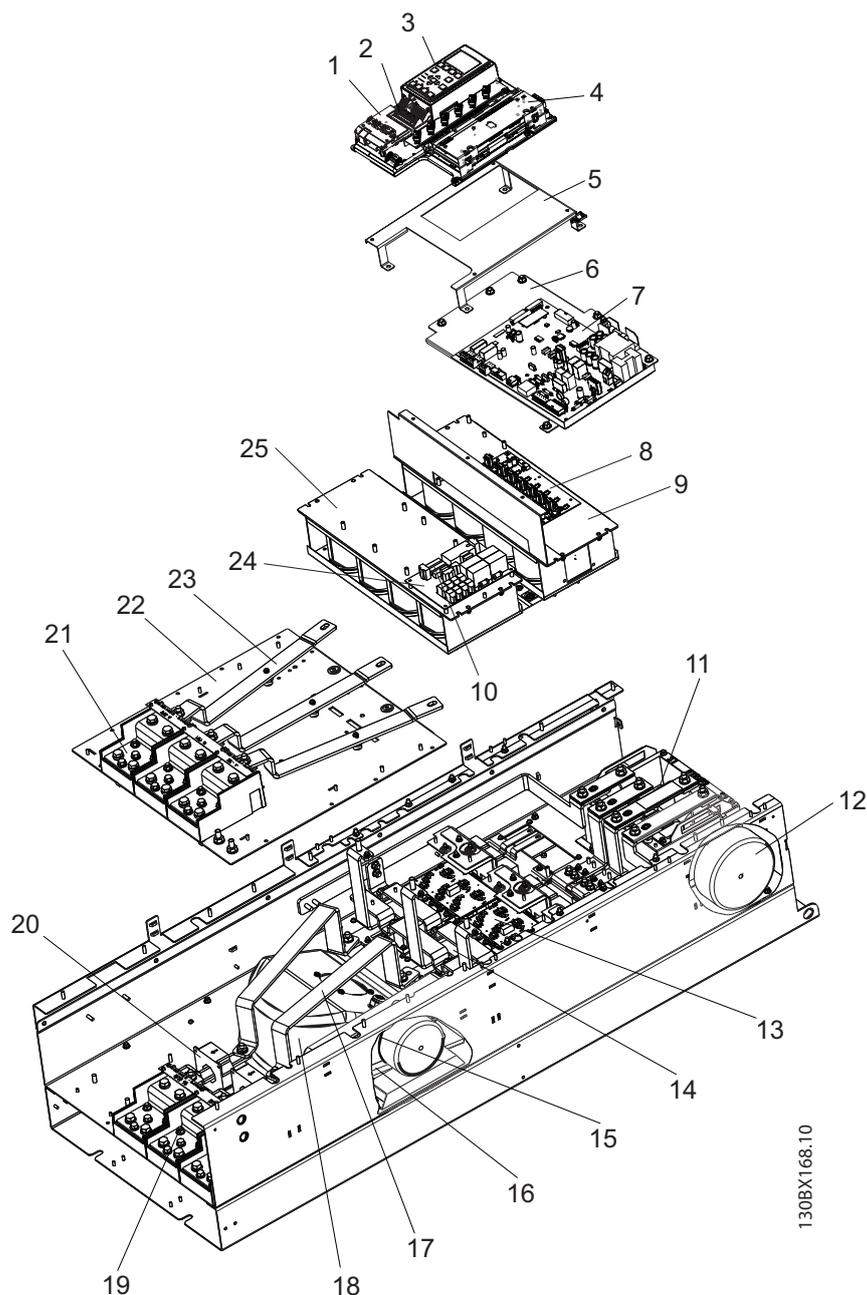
Vista explodida do chassi tamanho E2, chassi E1 é semelhante.
